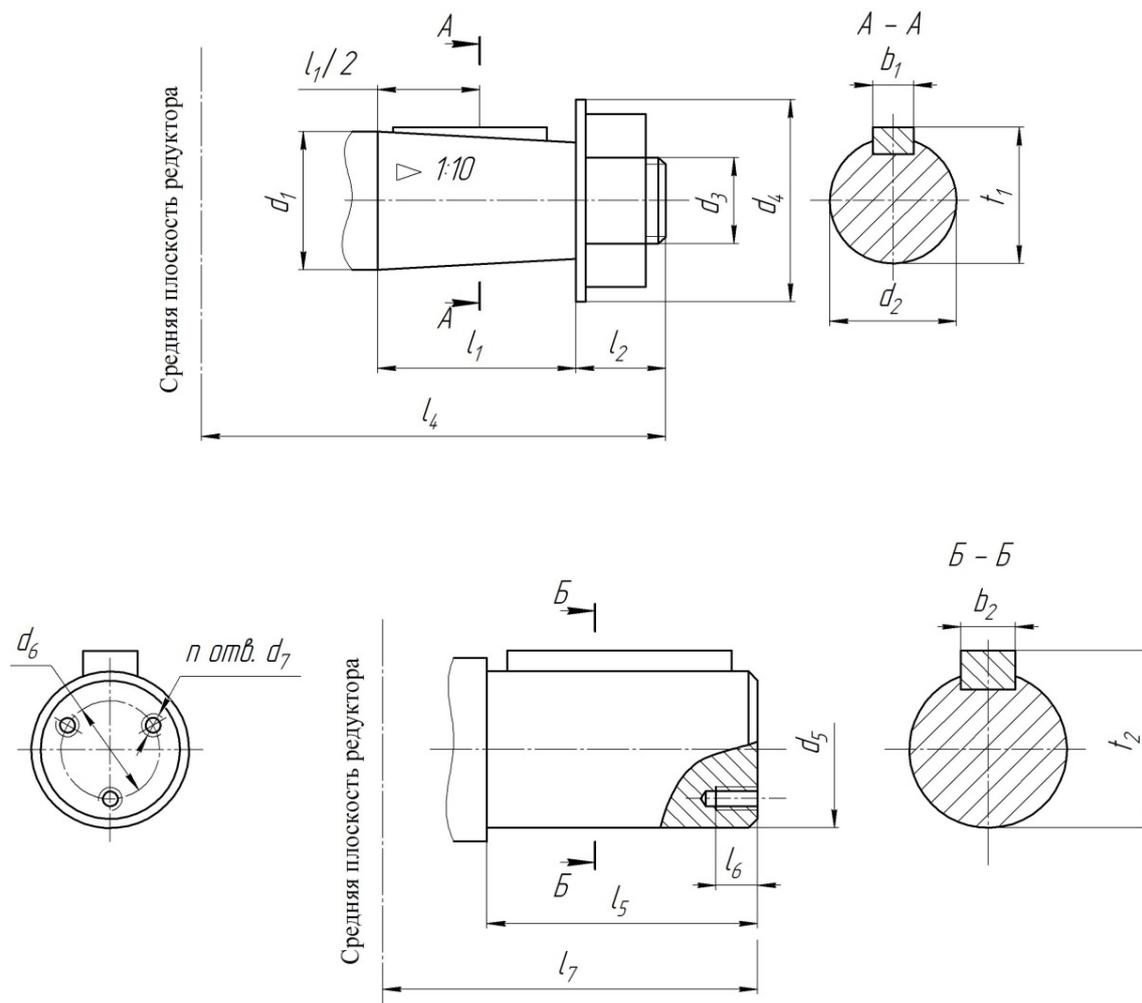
Конический и цилиндрический концы выходного вала редуктора
